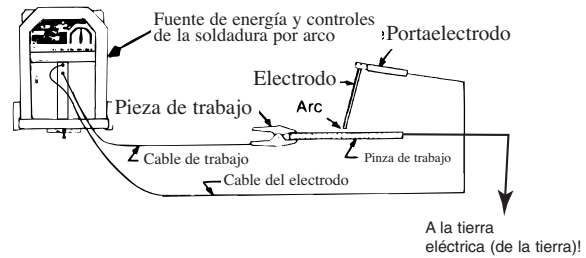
Circuito para la soldadura de arco con electrodo revestido
